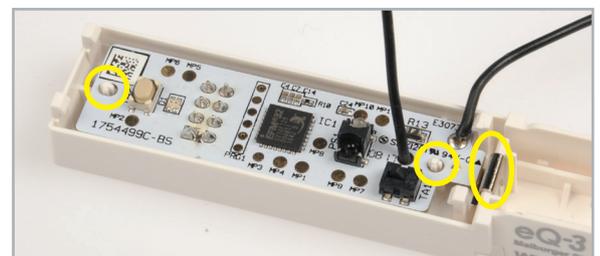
Die Montage beginnt mit dem Einsetzen der Platine in das Gehäuseunterteil. Die Gehäusedome müssen dabei durch die Platinenbohrungen und der Batteriekontakt über die Gehäusewand geführt werden.
